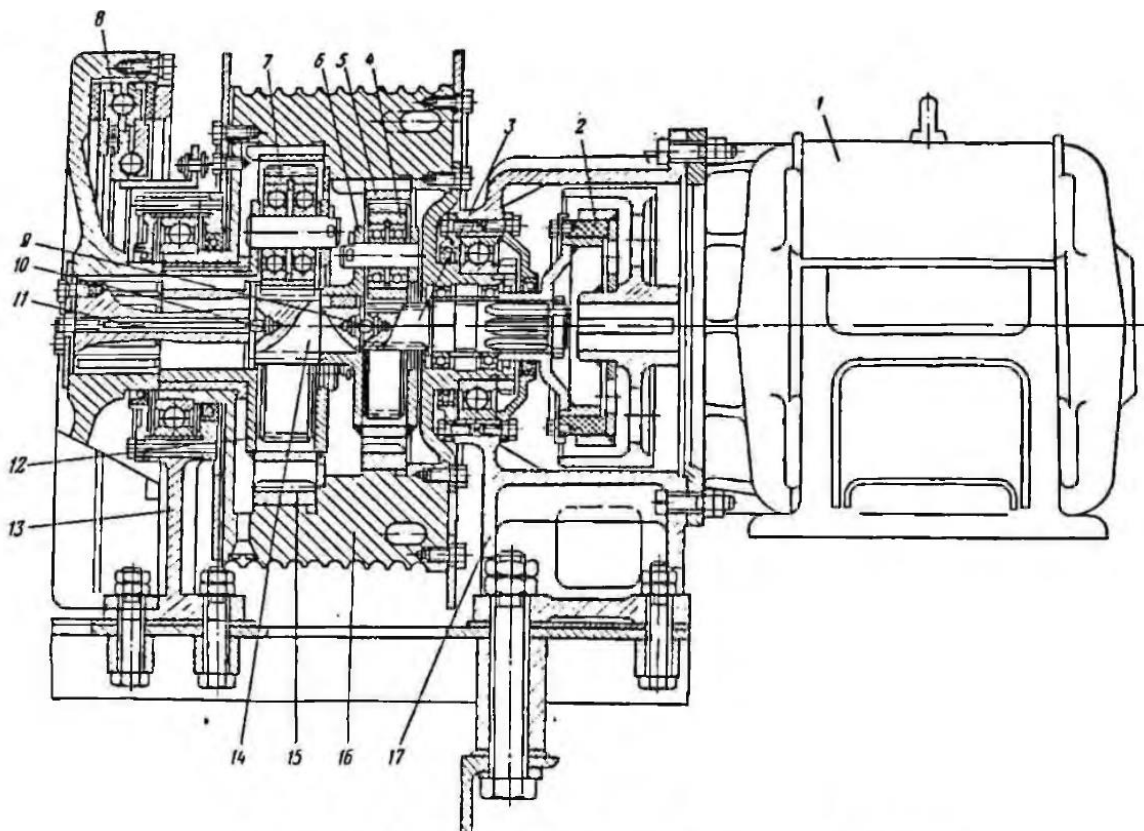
Двоступінчастий планетарний редуктор замкнутого типу приводу головної лебідки екскаватора Е-6516.
